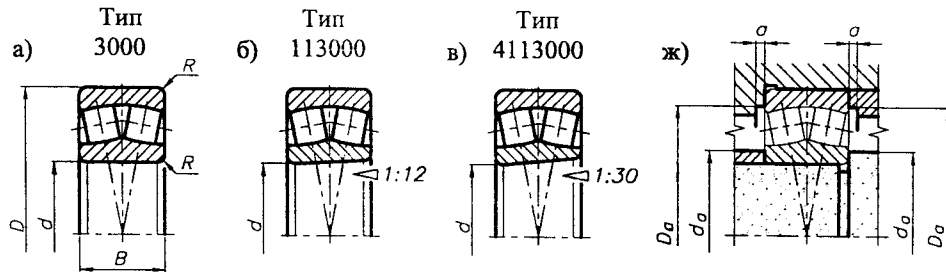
Габаритные и установочные размеры радиальных роликовых сферических двухрядных подшипников
